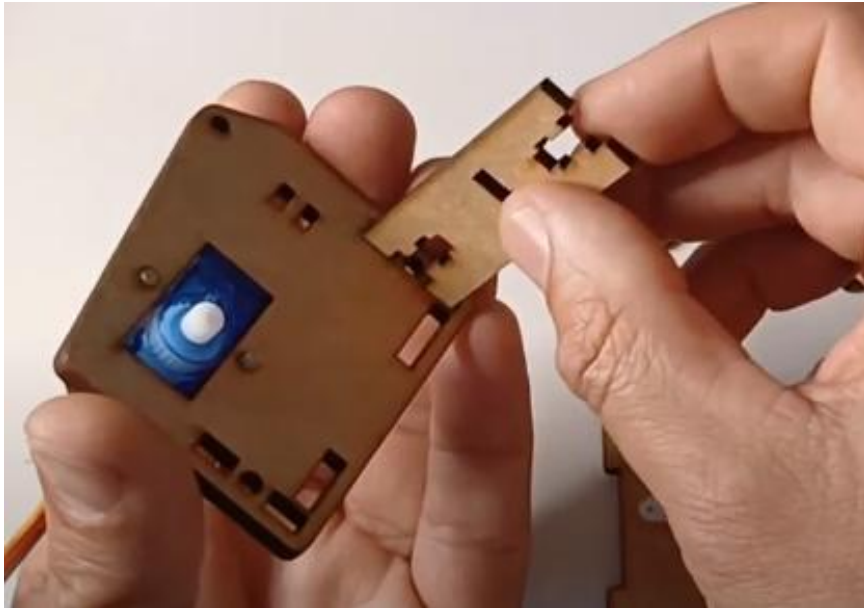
Montagem do Motor III e Suporte II - União das peças
